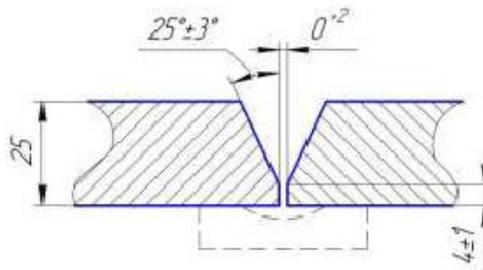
Конструктивные элементы подготовленных кромок сварного соединения
